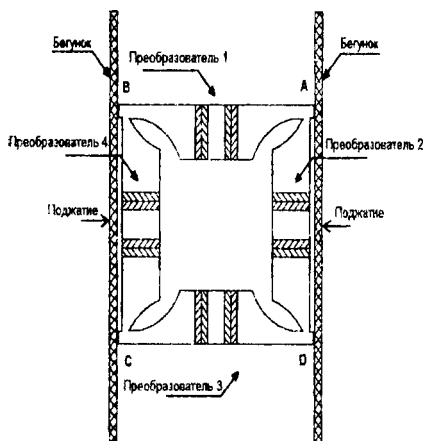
Общий вид статора пьезодвигателя специального вида
